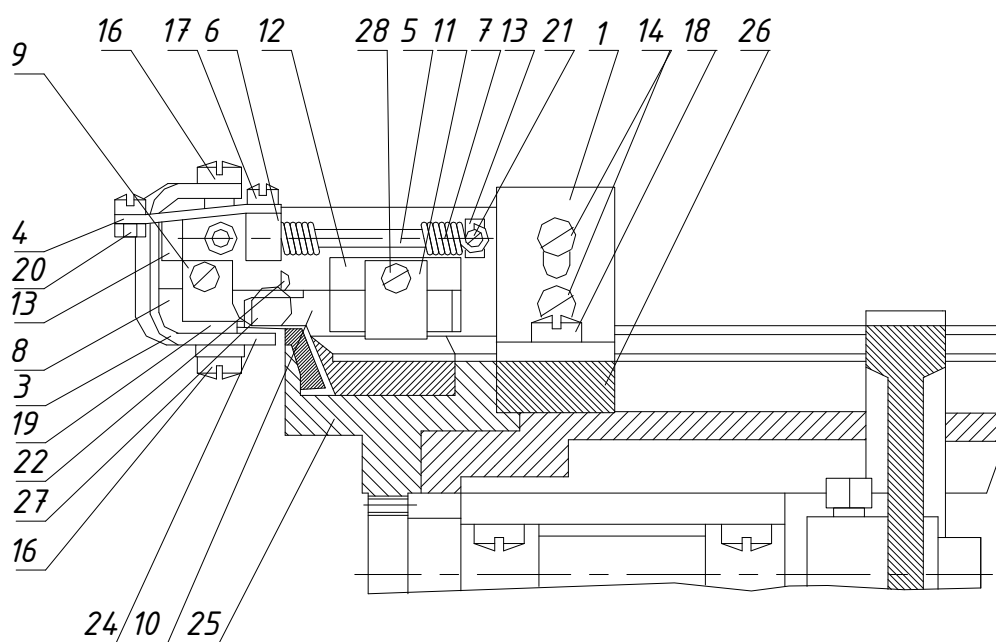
Механізм для кетельних машин для автоматичного розрізання нитки, вид збоку
